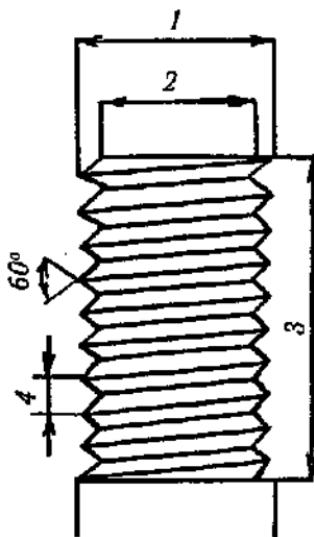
Параметры резьбы: 1 — наружный диаметр; 2 — внутренний диаметр; 3 — длина резьбы; 4 — шаг резьбы.
